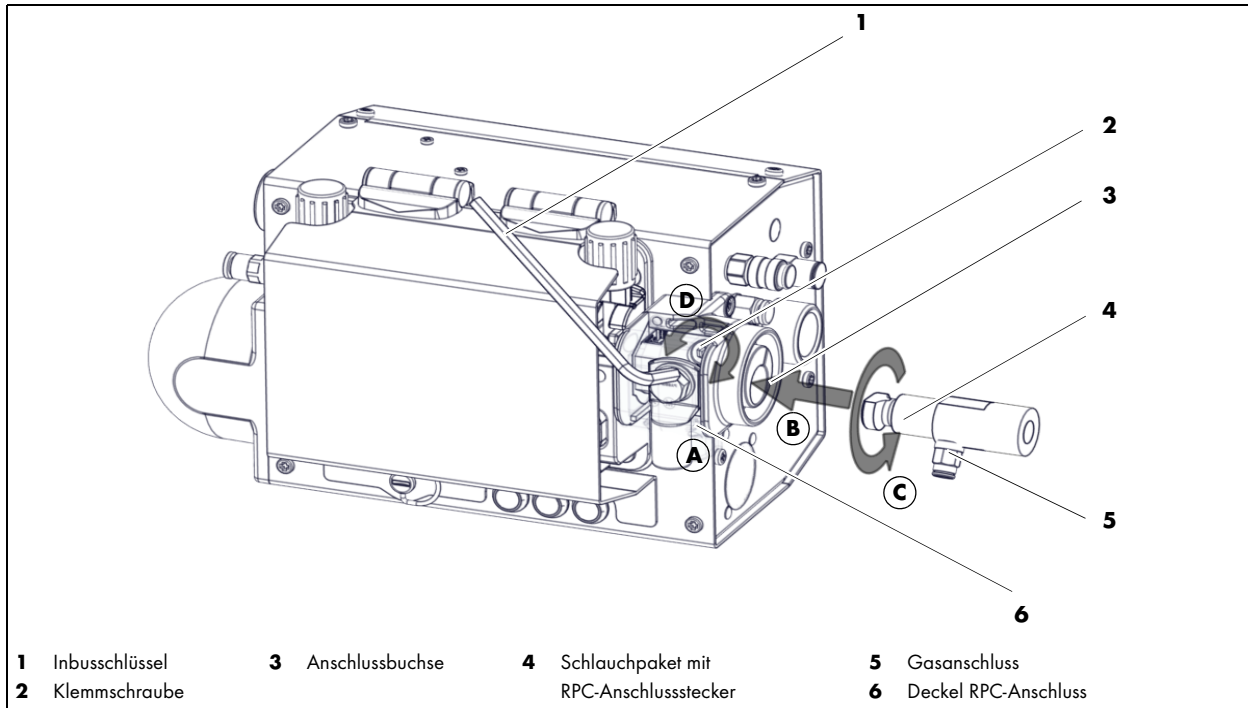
Schlauchpaket Schweißbrenner (RPC-Anschluss) iROB Feed 22 (Version mit Drahtvorschub rechts montiert)
